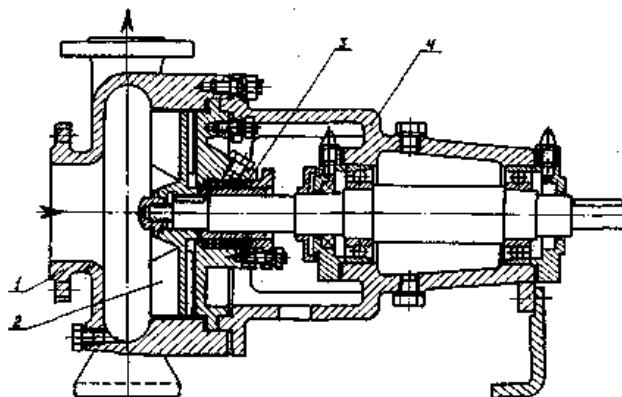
Конструкція вільновихрового насоса типу Turo. 1 — корпус; 2 — робоче колесо; 3 — ущільнення кінцеве; 4 — корпус підшипників.
